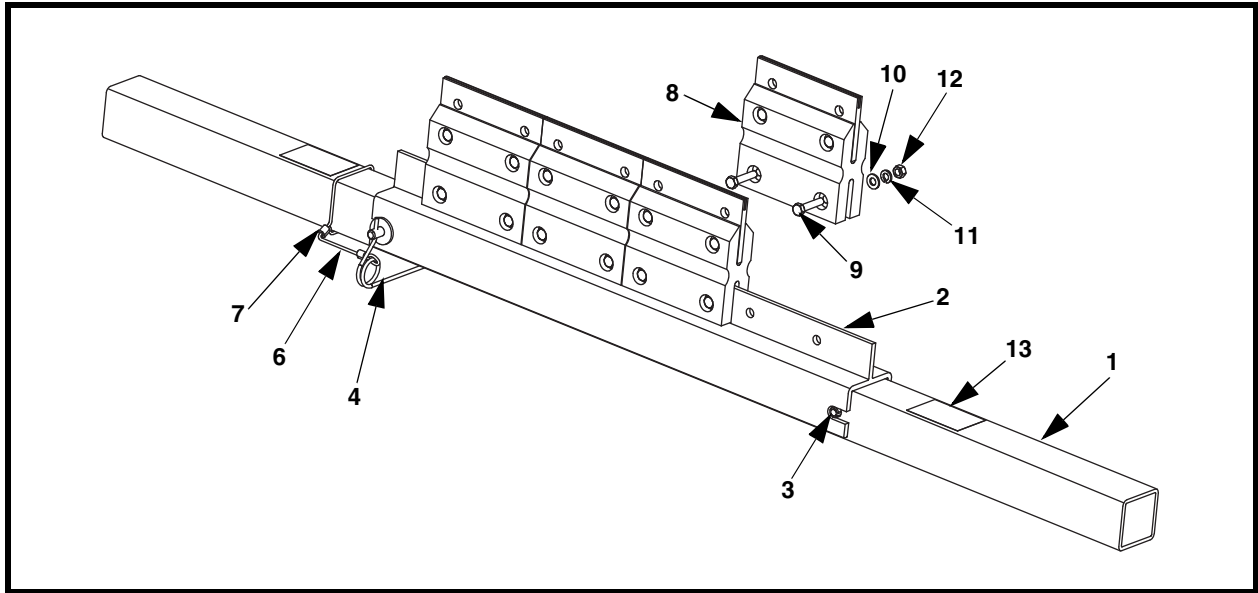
Conjunto de Limpador Martin® SQC2S™, P/N SQC2S-XXXXXXXXXX
